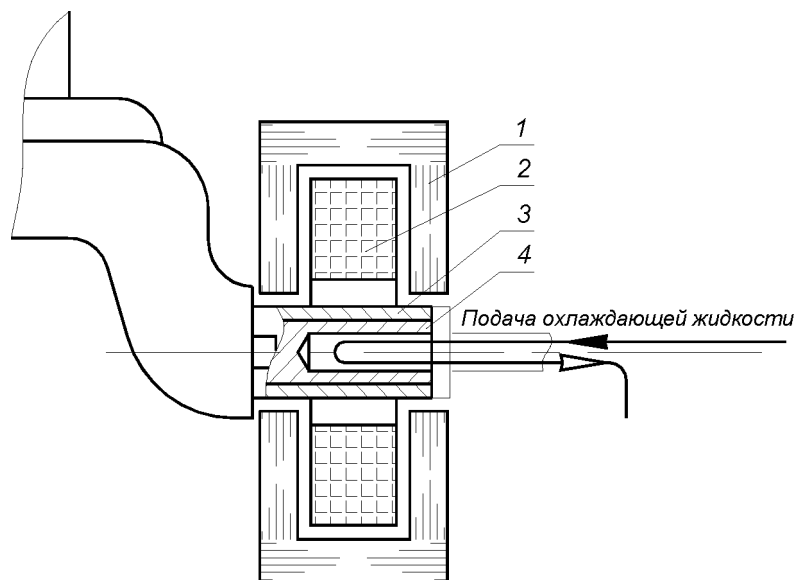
Схема установки для съема втулки с карданного вала:
